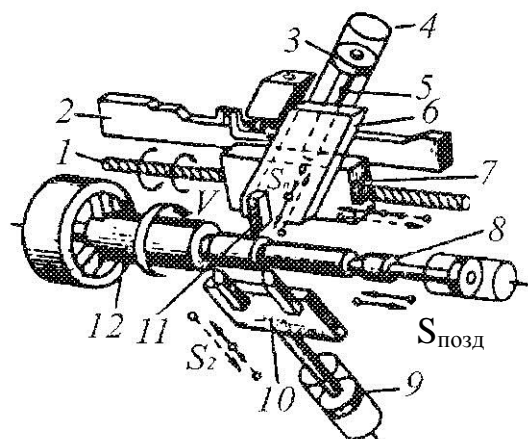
Схема роботи гідрокопіювального напівавтомата
